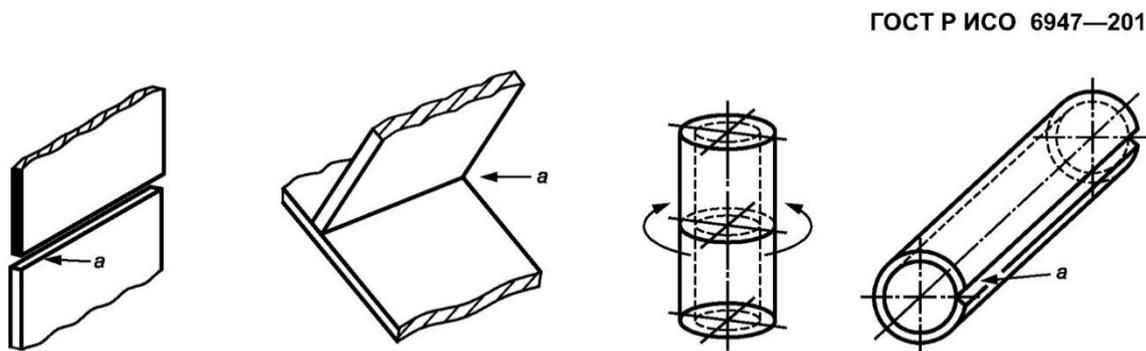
РС – положение горизонтальное. а – стрелка указывает положение при сварке.
